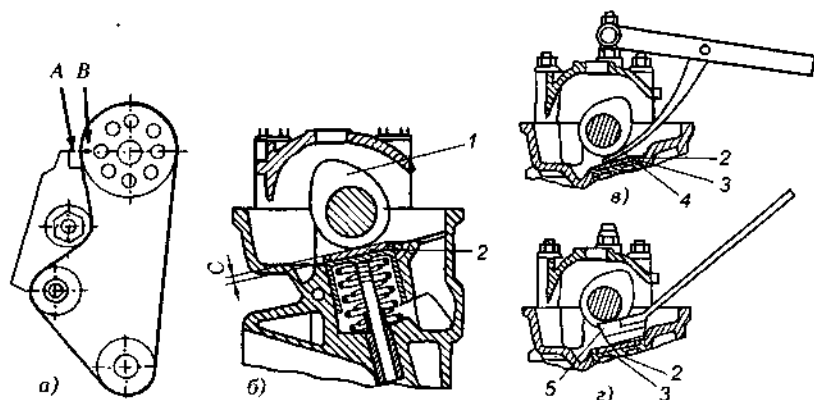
Регулировка тепловых зазоров ГРМ переднеприводных автомобилей марки «ВАЗ»: а — совмещение меток; б — проверка зазора; в — утапливание толкателя; г — фиксация толкателя в нижнем положении; А — метка на задней крышке; В — метка на шкиве распредвала; С — регулируемый зазор; 1 — кулачок; 2 — регулировочная шайба; 3 — толкатель; 4 — упор; 5 — фиксирующее приспособление
